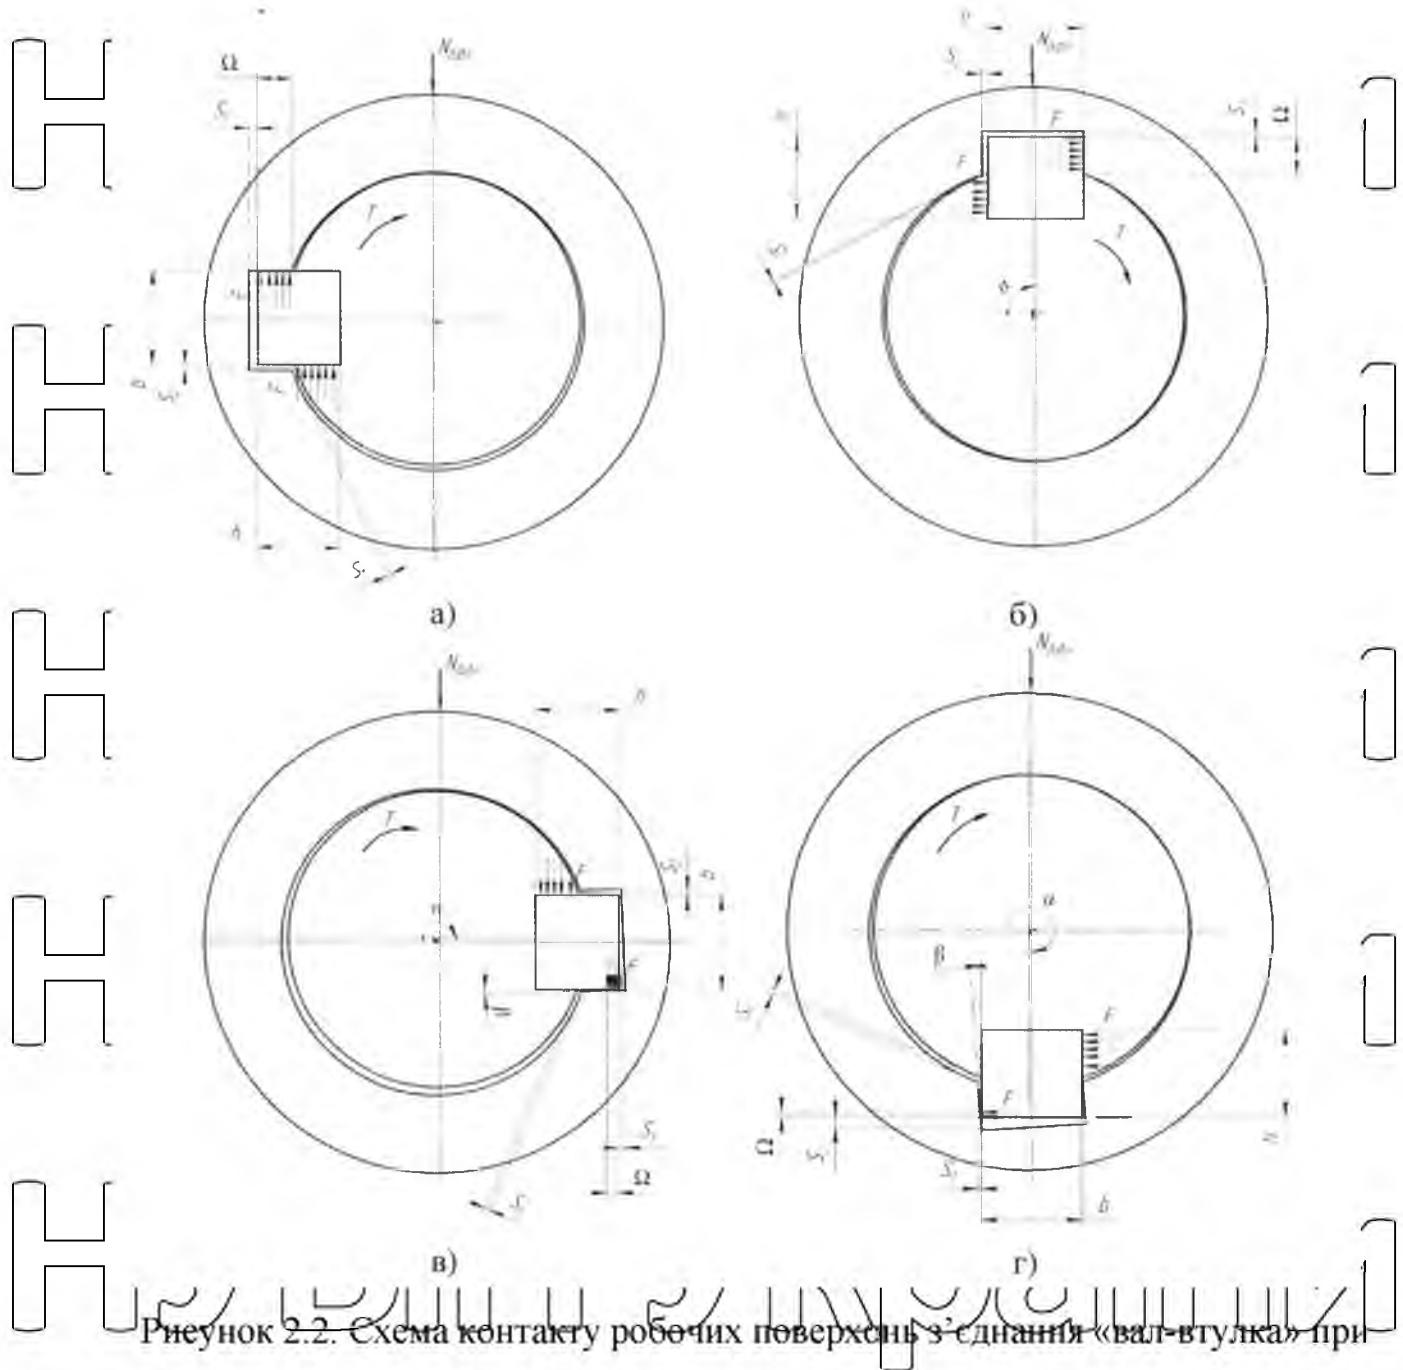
Схема контакту робочих поверхонь з'єднання «вал-втулка» при обертанні: а) при 0° ; б) при 90° ; в) при 180° ; г) при 270° .
